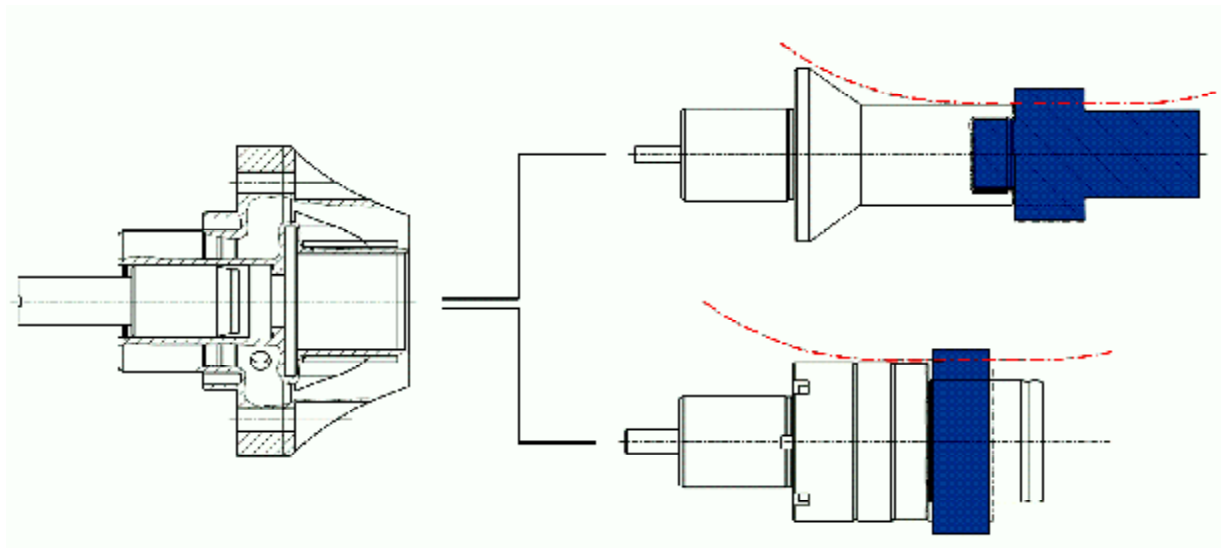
Prinzip-Skizze des Schnellwechselfutters am Beispiel für Reishauer RZ 150. Links: Grundaufnahme, rechts oben: Adapter für Wellen, rechts unten: Adapter für Bohrungen. Rot: Störkontur des Schleifwerkzeugs.
